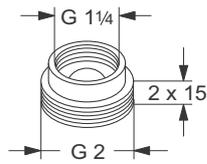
Beispiel für ein Gewinde/Gewinde-Adapter
